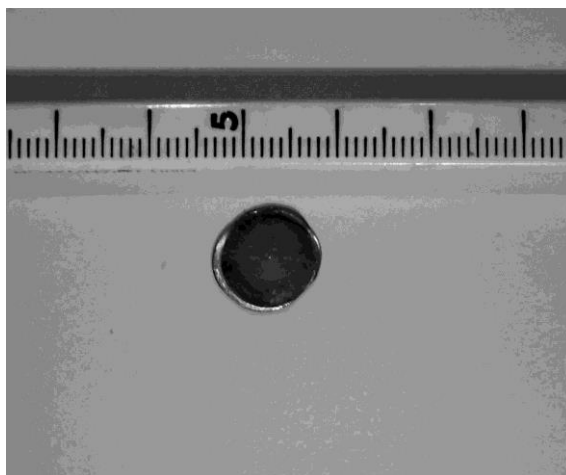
Внешний вид заготовки стали после КВД
